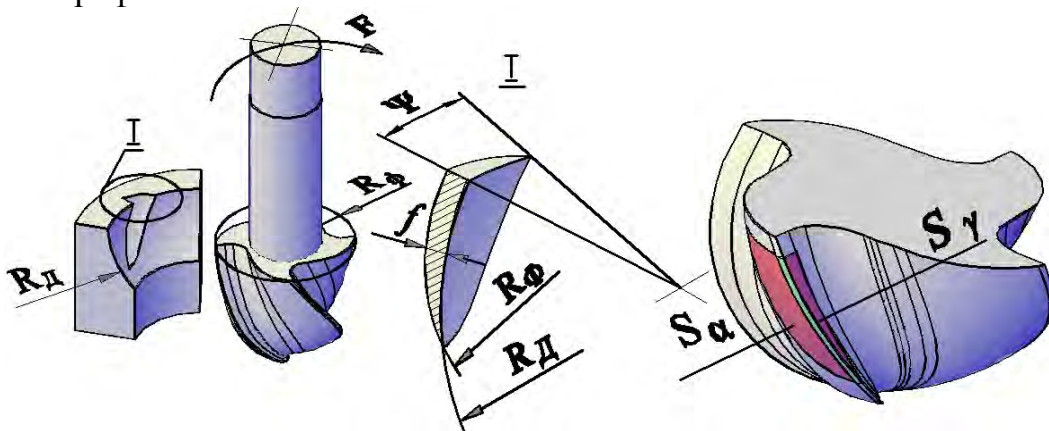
Формування перетину зрізу заготовки R_d товщиною f фрезою R_ϕ
